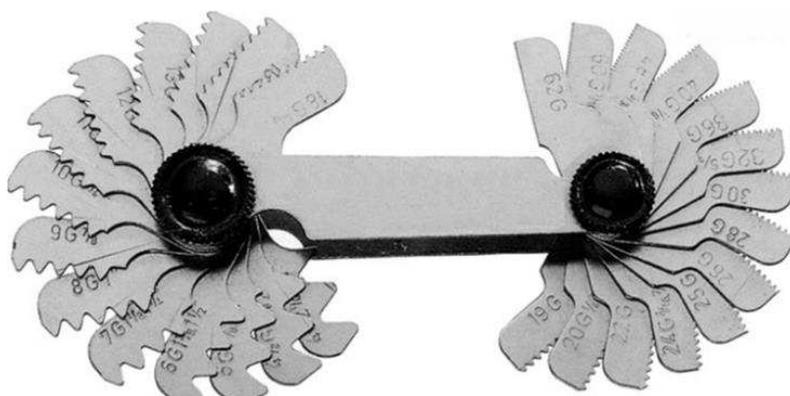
Внешний вид набора резьбовых шаблонов
